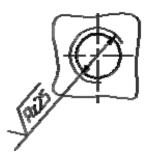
Пример обозначения шероховатости внутренней резьбы
